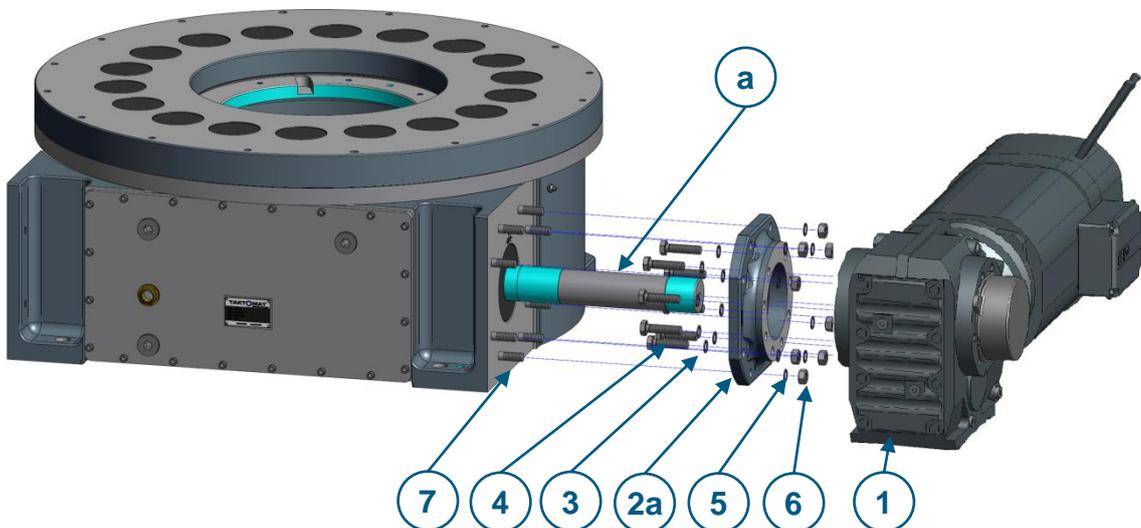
Anbau Komplettantrieb mit Guss - Antriebsflansch
